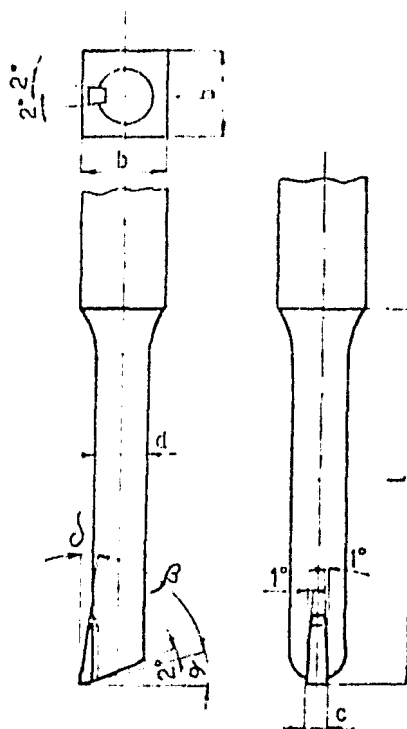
Herramienta con plaquita de metal duro para mortajar una entalla para chaveta.
